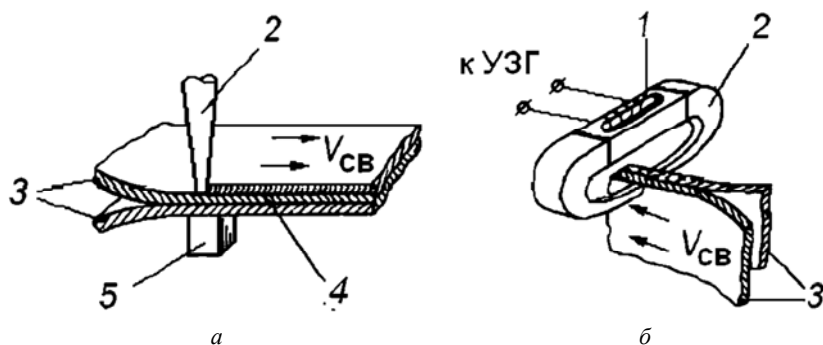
Схемы шовной сварки «на протяг» с подводом ультразвуковых колебаний:
